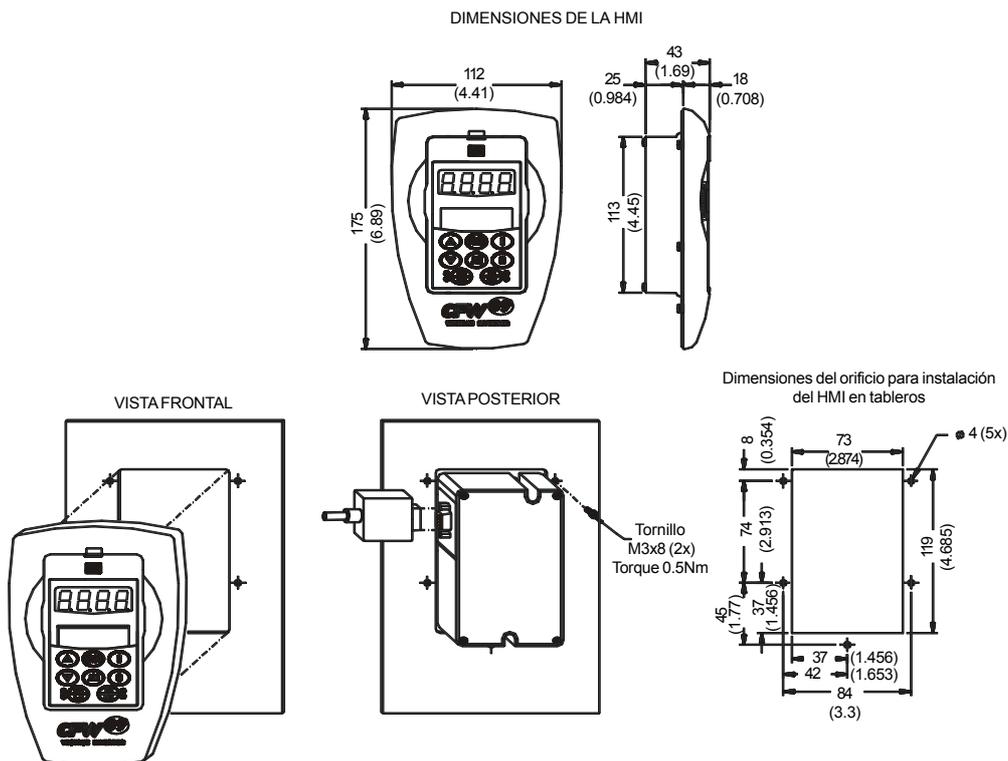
b) y c) - Dimensiones en mm (in) y como instalar en el tablero HMI y Moldura
